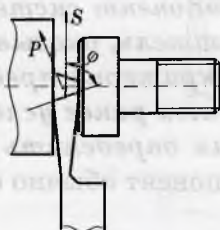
Схема отрезания детали от групповой заготовки резцом с углом в плане  $\varphi < 90^\circ$
